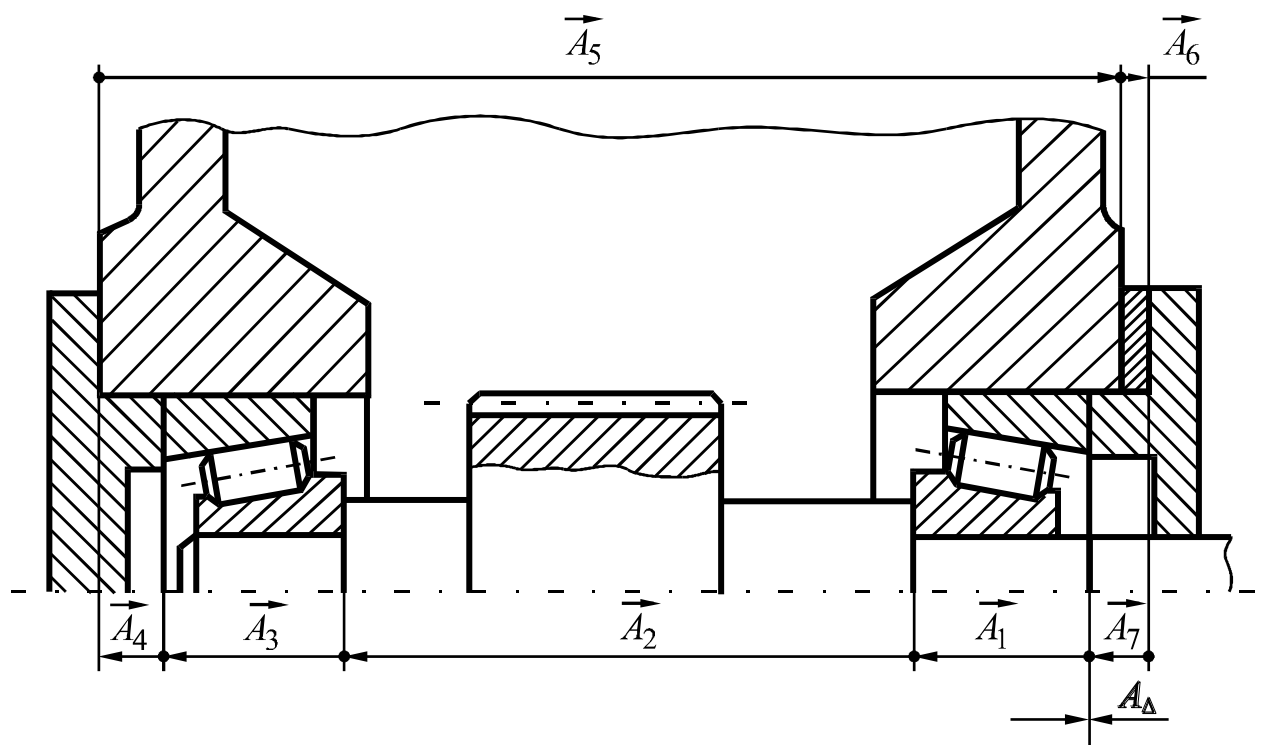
Размерная цепь вала шестерни редуктора, установленного в конических роликоподшипниках
